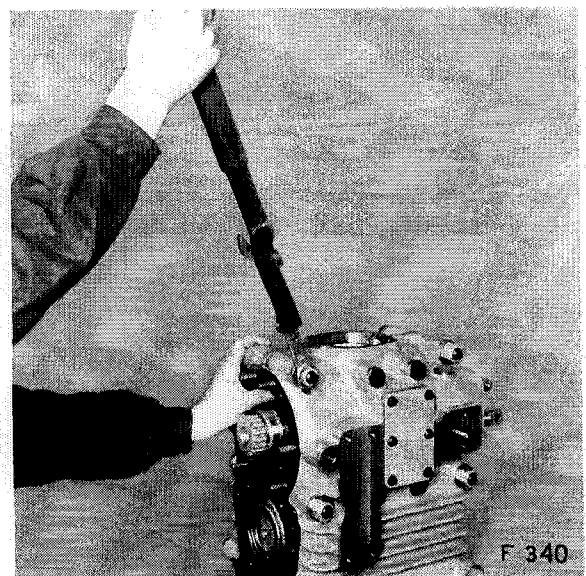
Entfernen des Seegerrings vor dem Kugellager
